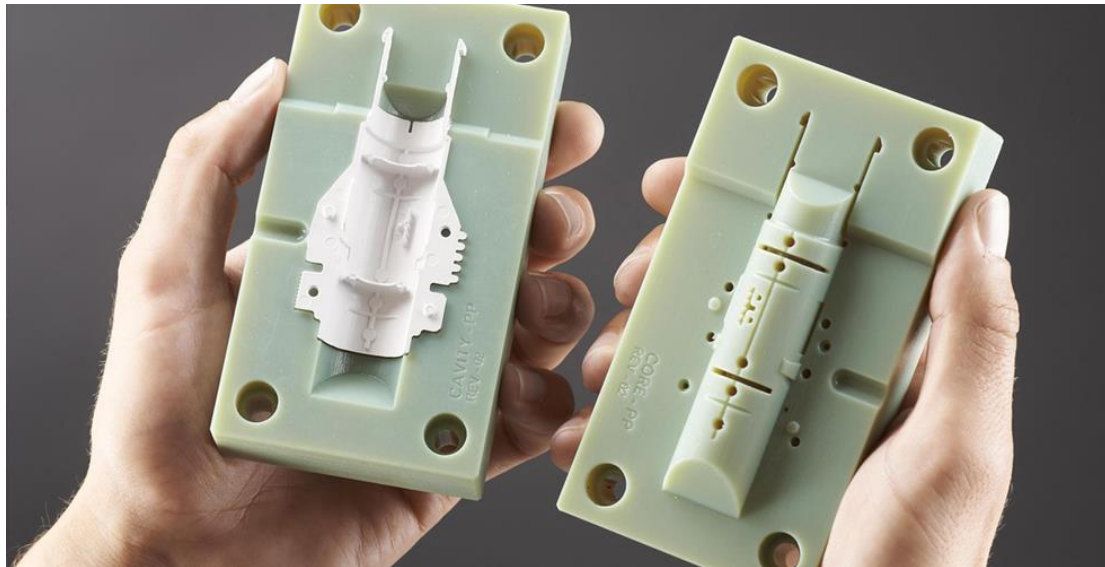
Molde fabricado por impressão 3D para o processo de injeção.
